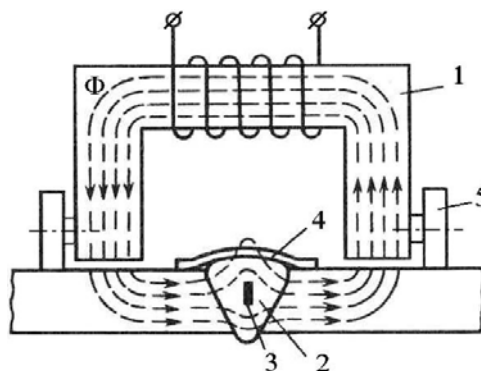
Схема магнітографічного контролю зварювального шва: 1 – пристрій намагнічування, 2 – зварювальний шов, 3 – дефект, 4 – магнітна плівка, 5 – коліщатко
